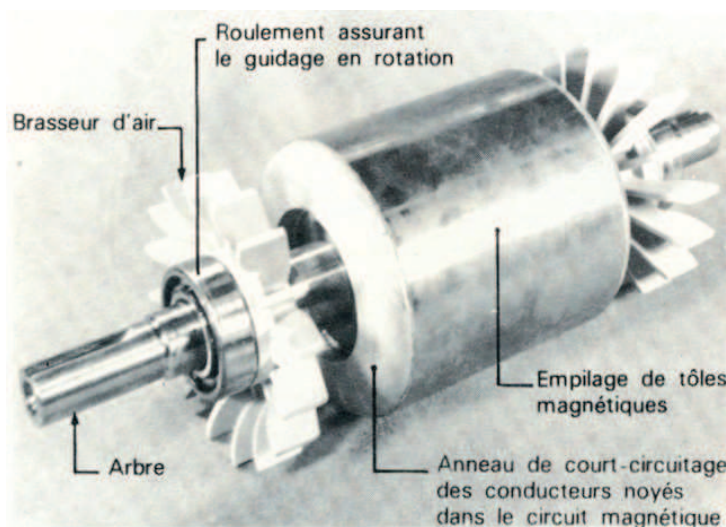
Rotor à cage d'écureuil (vue d'ensemble)
